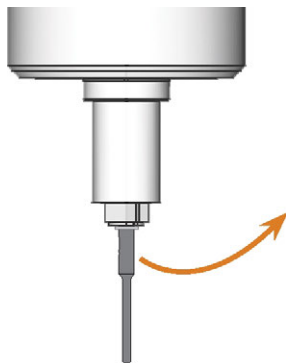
RETIRER L'OUTIL DE LA PINCE DE SERRAGE
